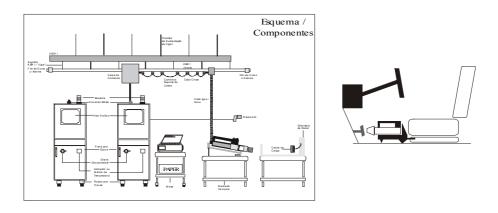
Equipamento a prova de erros para o ajuste do cabo da embreagem
